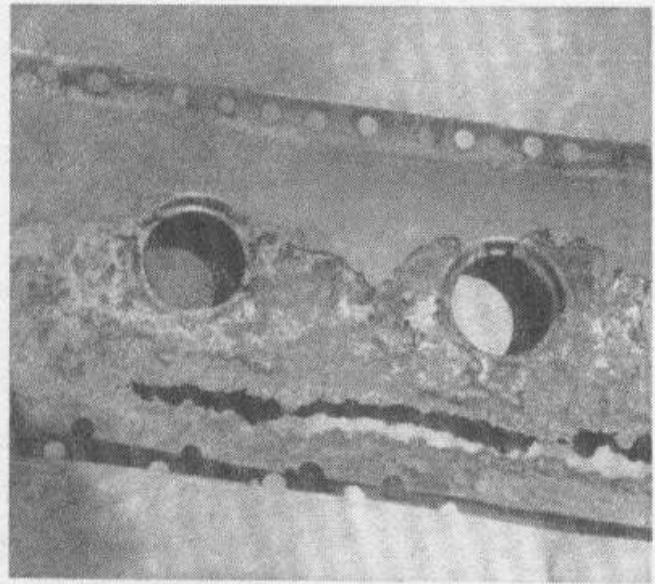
Typische Korrosion am Mittelsteg des Lada-Längsträgers unmittelbar über der Punktschweißverbindung; die Schweißpunkte wurden zwecks Demontage freigebohrt
